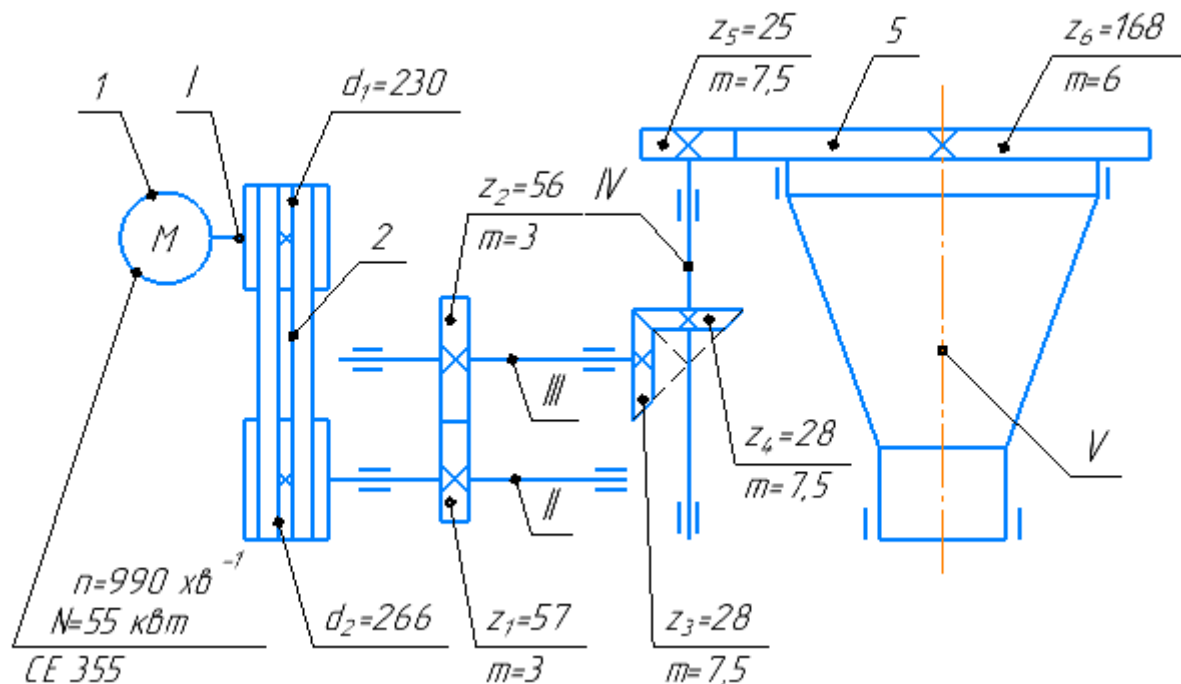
Кінематична схема модернізованого механізму повороту токарно-карусельного верстата 1516
